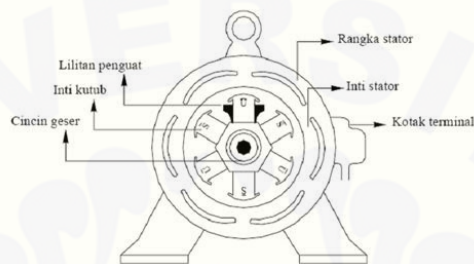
Konstruksi umum motor induksi 1 fasa (Sumber: Sinaga, 2011)
